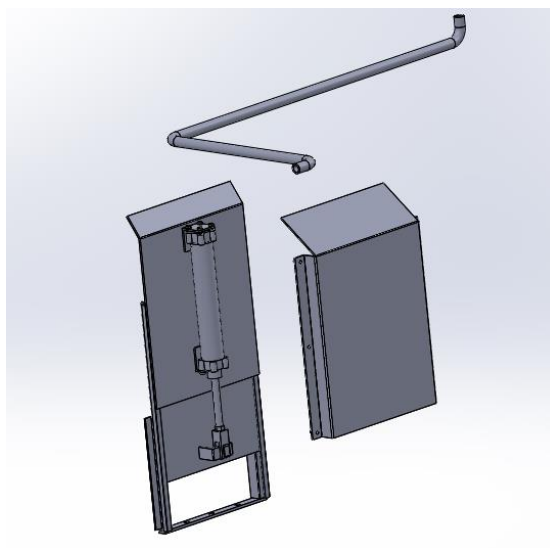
Subensamblaje del portillón neumático.
